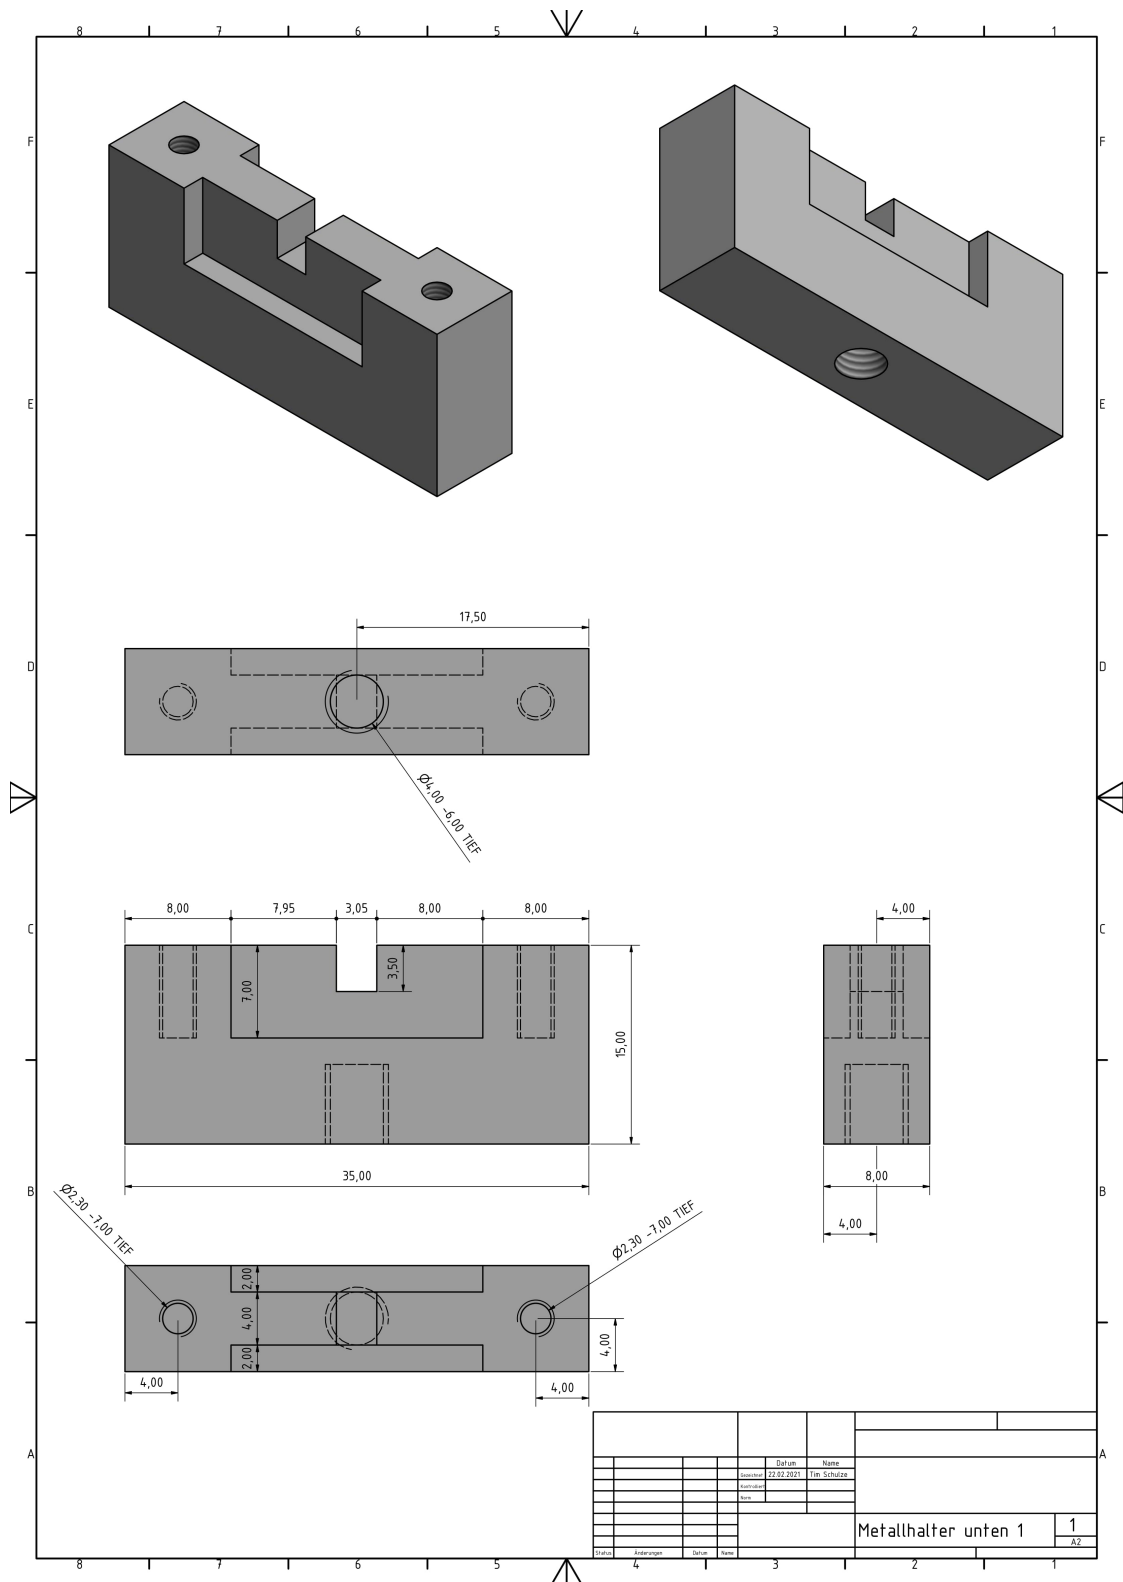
Technische Zeichnung des unteren gefrästen Metallhalters für die statischen Wellenleiter
